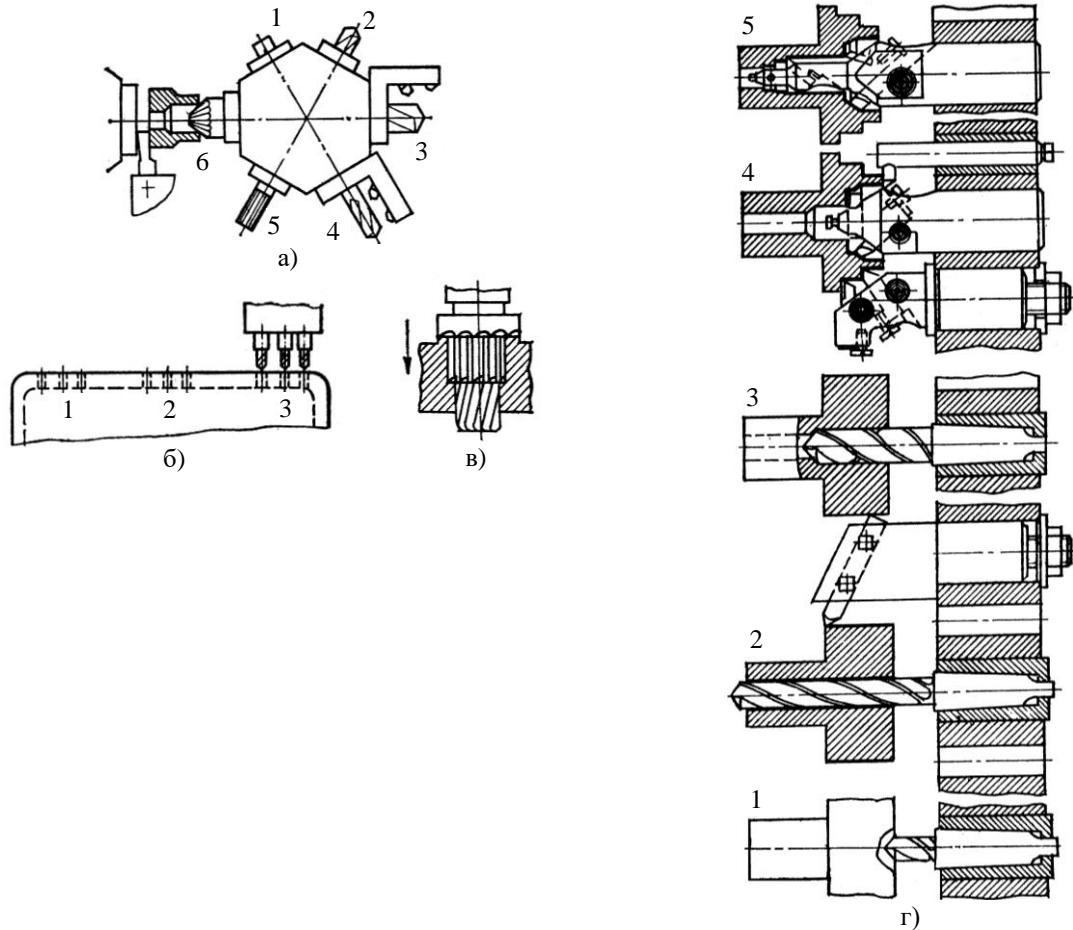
Схема одномісної паралельно-послідовної багатоінструментної обробки:
